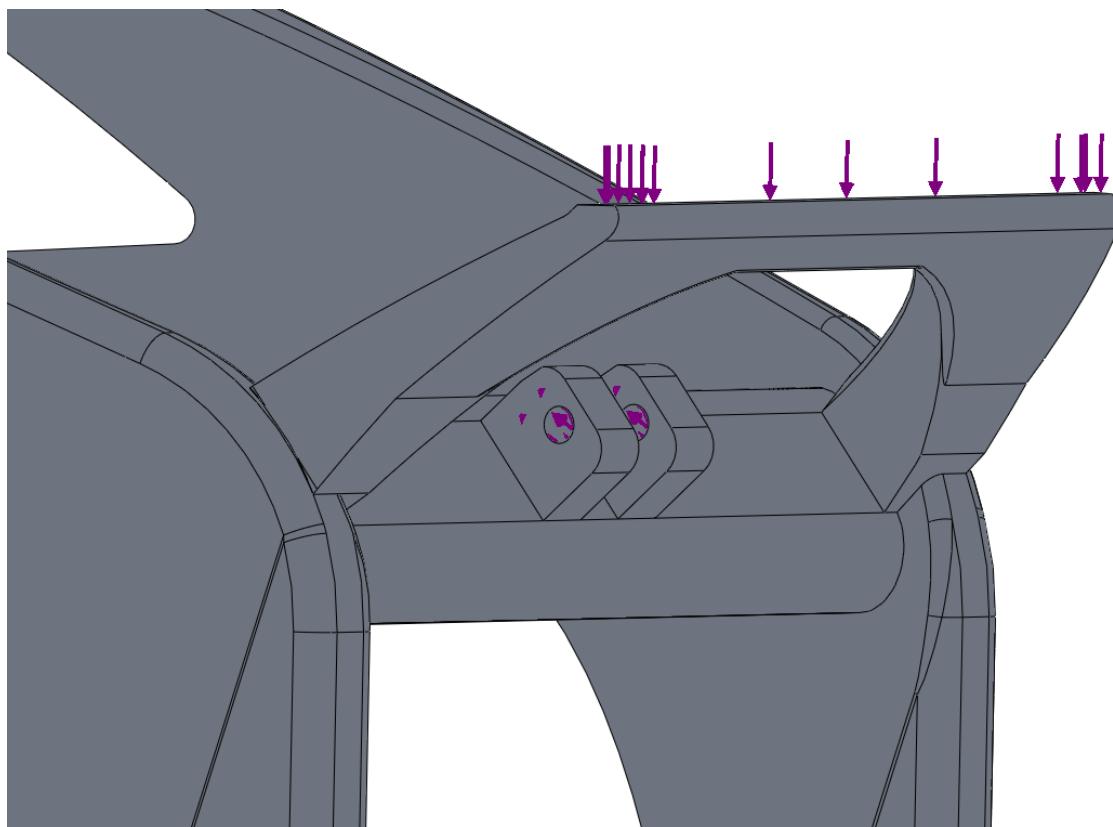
Vista detalle fuerzas suspensión y peso piloto
